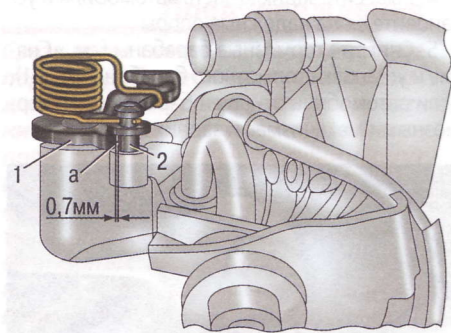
Контрольный зазор привода стояночного тормоза автомобиля, оснащенного дисковыми тормозными механизмами задних колес: а – контрольный зазор между разжимным рычагом и опорой суппорта; 1 – разжимной рычаг; 2 – опора суппорта заднего тормозного механизма
